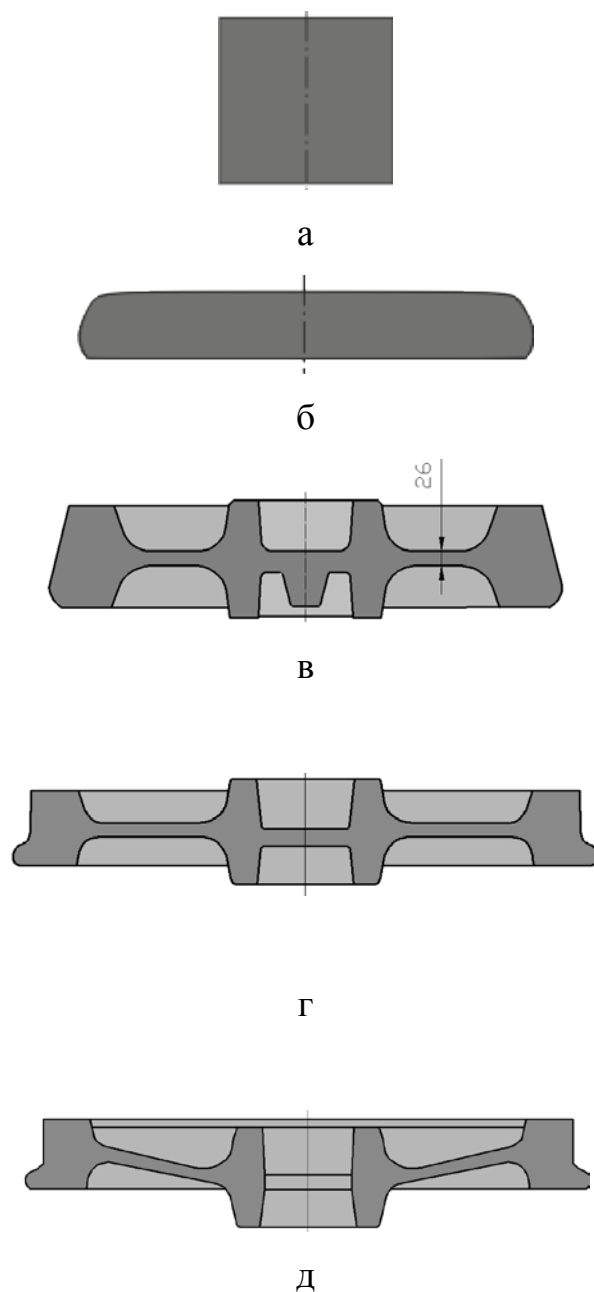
Схема деформации заготовки на прессо- прокатной линии ОАО «НТМК»: а – исходная заготовка, б – обжатие заготовки в кольце на прессе 50 МН, в – формовка на прессе 90 МН, г –раскатка на колесопркатном стане, д – выгибка диска, калибровка обода и прошивка отверстия в ступице колеса на прессе 50 МН
